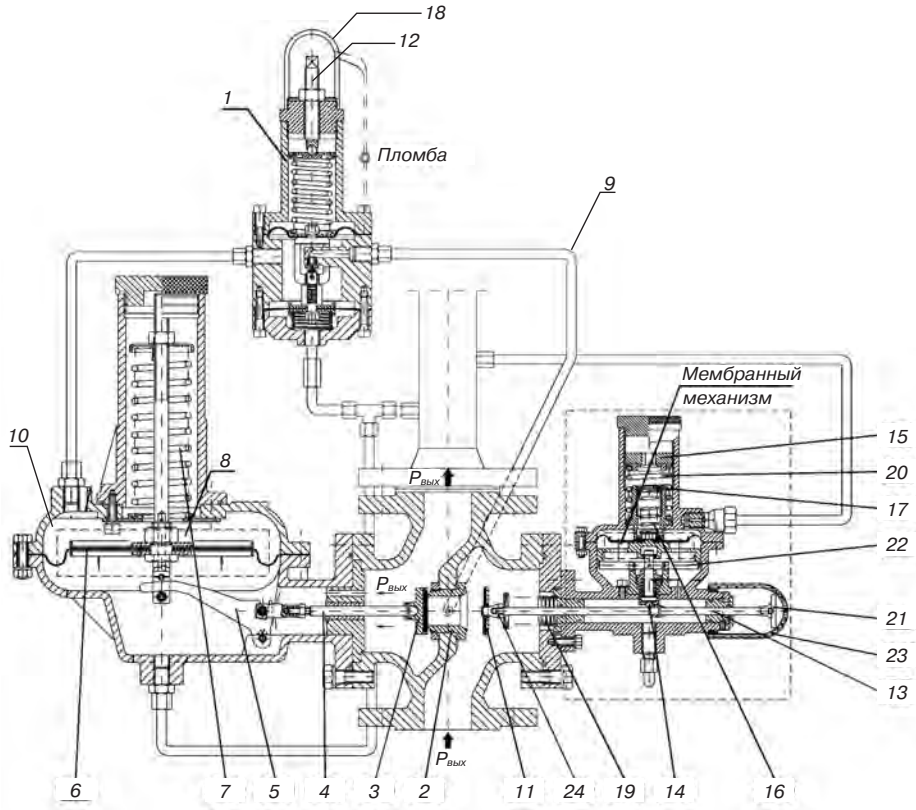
Регулятор давления с предохранительно-запорным клапаном 131-BV: 1 — пилот регулятора; 2 — седло; 3 — клапан; 4 — шток; 5 — рычаг; 6 — мембрана; 7, 16, 19, 20 — пружина; 8 — мембранный механизм; 9 — импульсная трубка; 10 — мембранная полость; 11 — клапан; 12 — регулировочный винт пилота; 13 — шток; 14 — стопорный шарик; 15, 17 — гайка; 18, 23 — колпачок; 21 — ручка; 22 — рычаг
